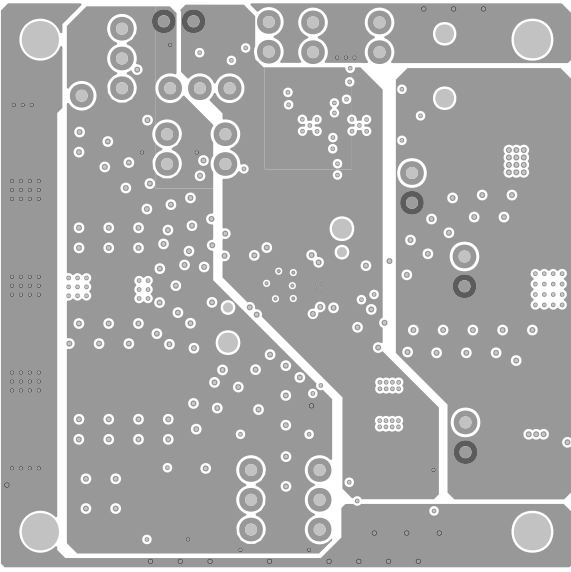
TUSB2E221EVM PCB 第 3 层 (电源平面)
